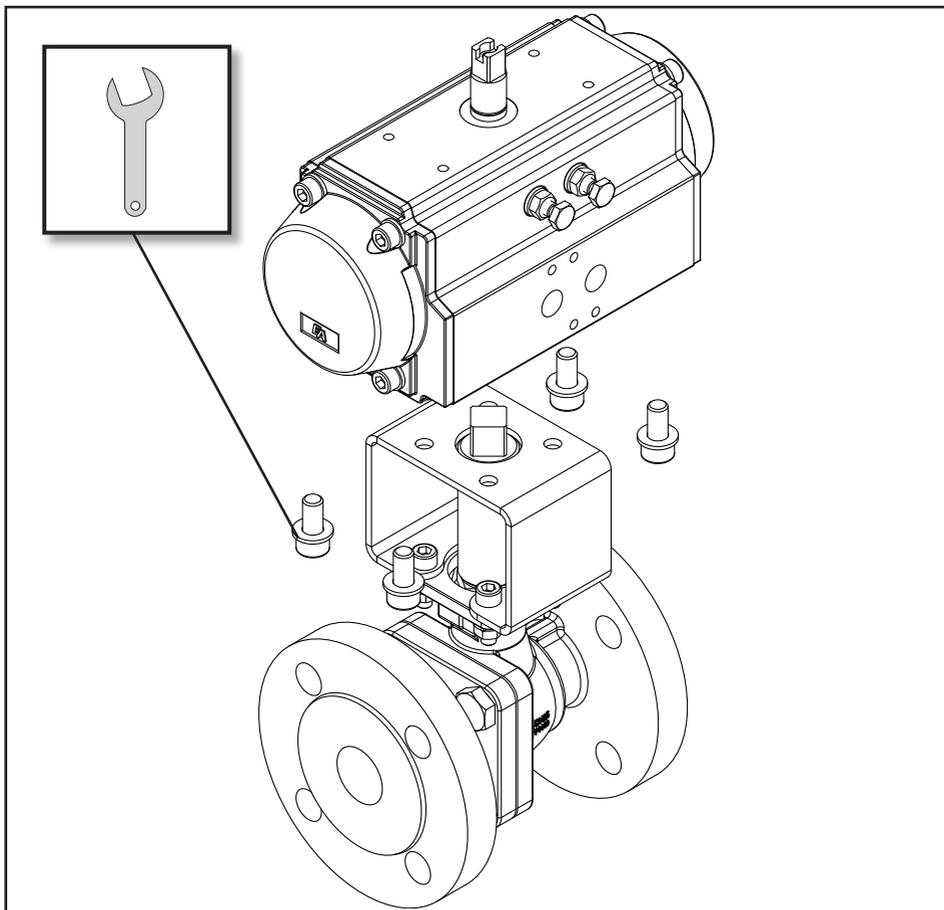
Montage / Demontage, Montage mittels Konsole und Spindel
